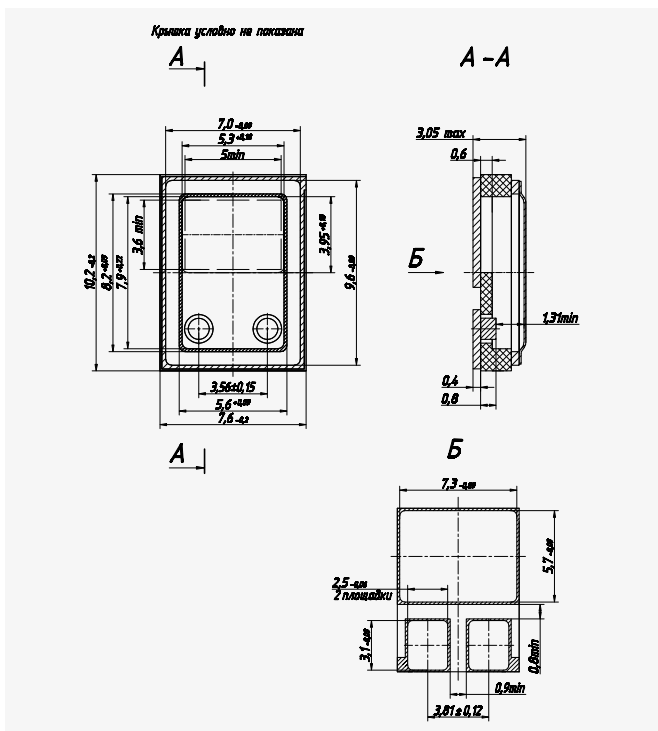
Габаритный чертеж металлокерамического корпуса KT-93
